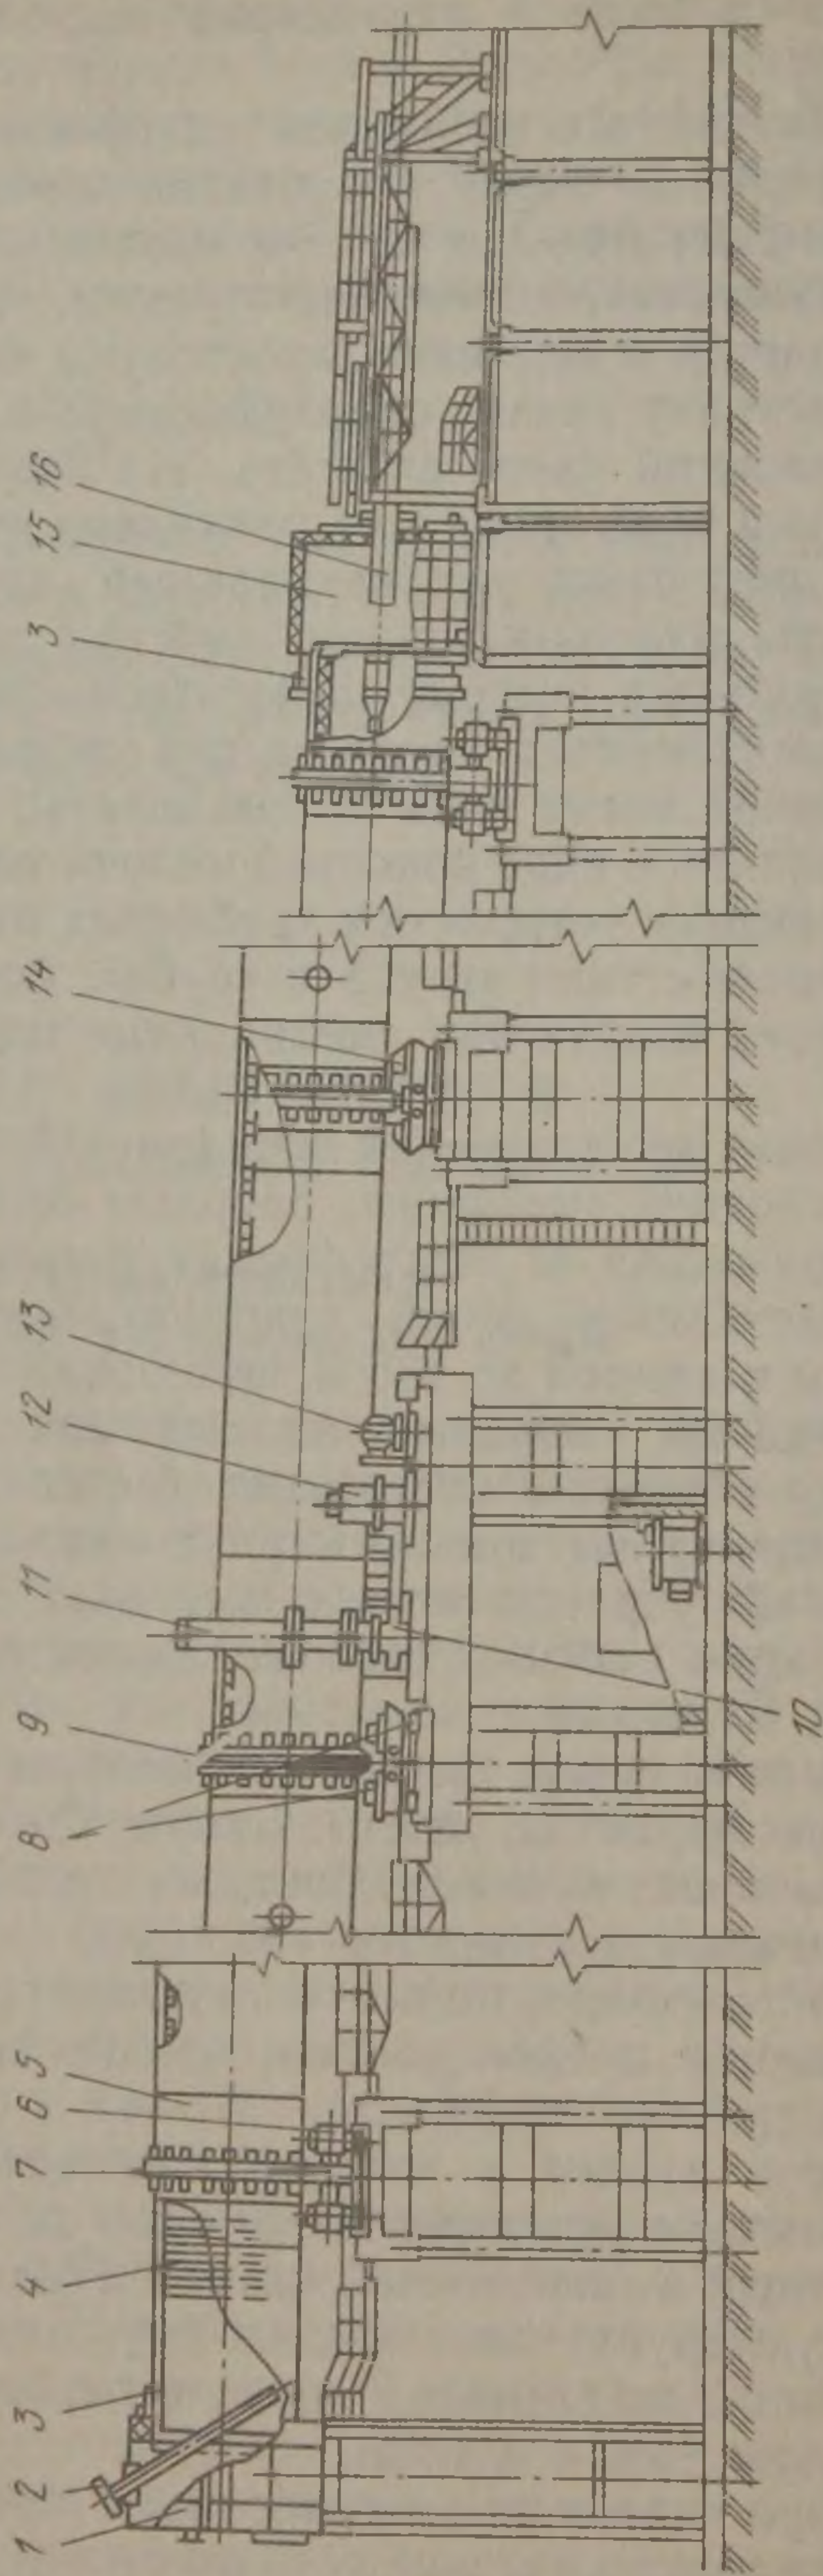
Общий вид вращающейся трубчатой печи:
